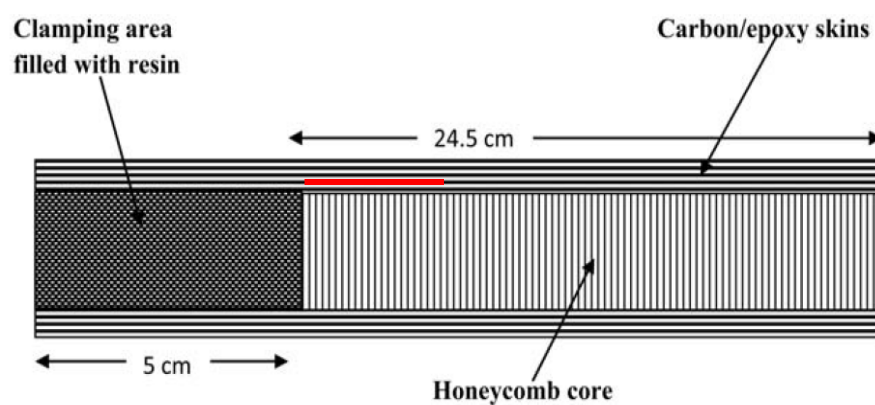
Section d'une poutre (Fotsing, Sola, Ross, & Ruiz, 2012)
